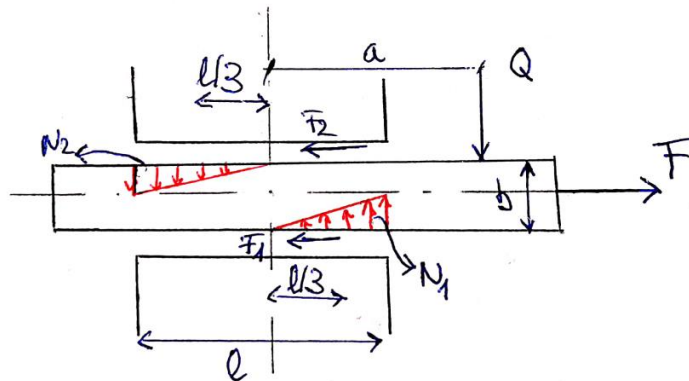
Planteamiento para la deducción del cálculo de la fuerza de rozamiento
